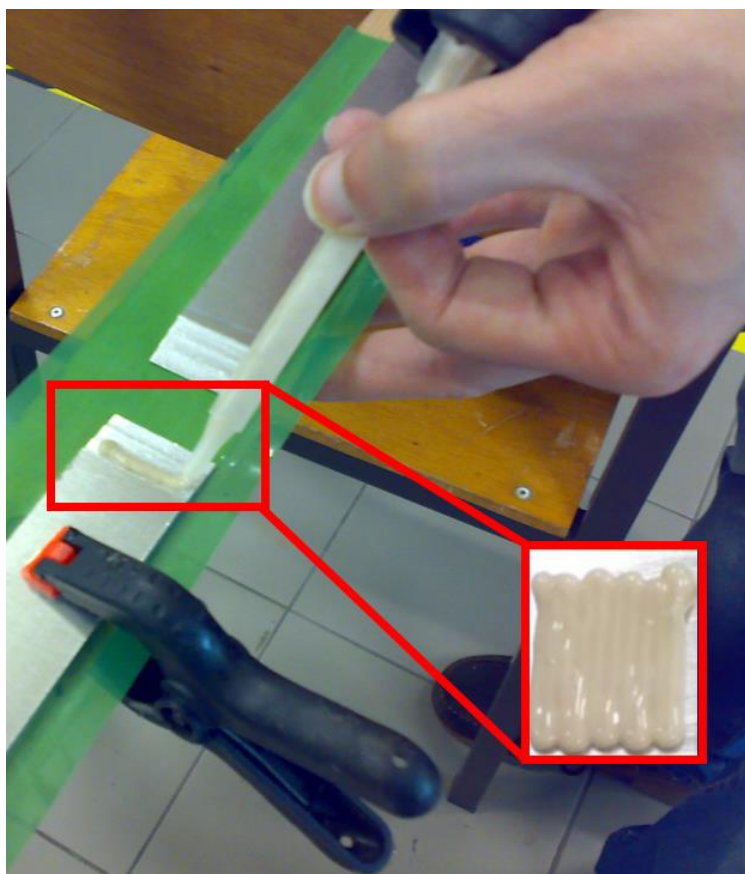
Pormenor de aplicação adesivo Araldite® 2015.
